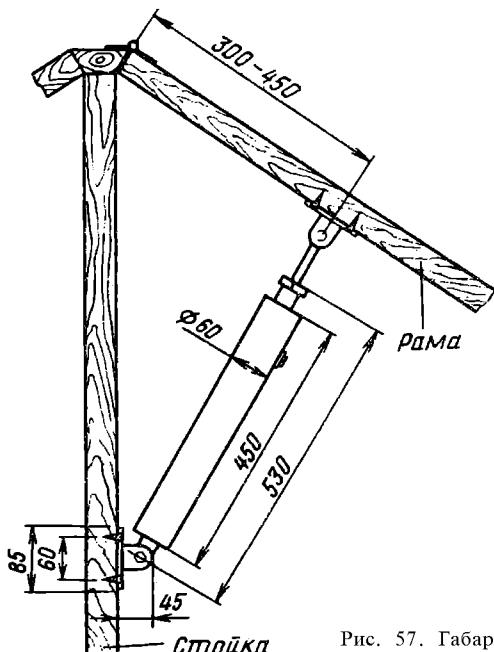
Габаритные и установочные размеры регулятора "Тюльпан"
